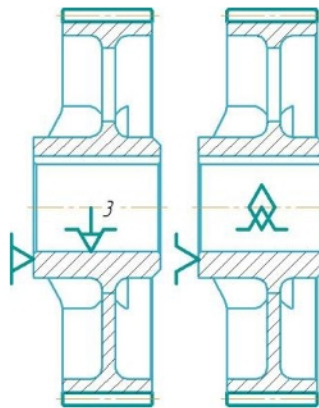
Умовна та теоретична схема базування зубчастого колеса
